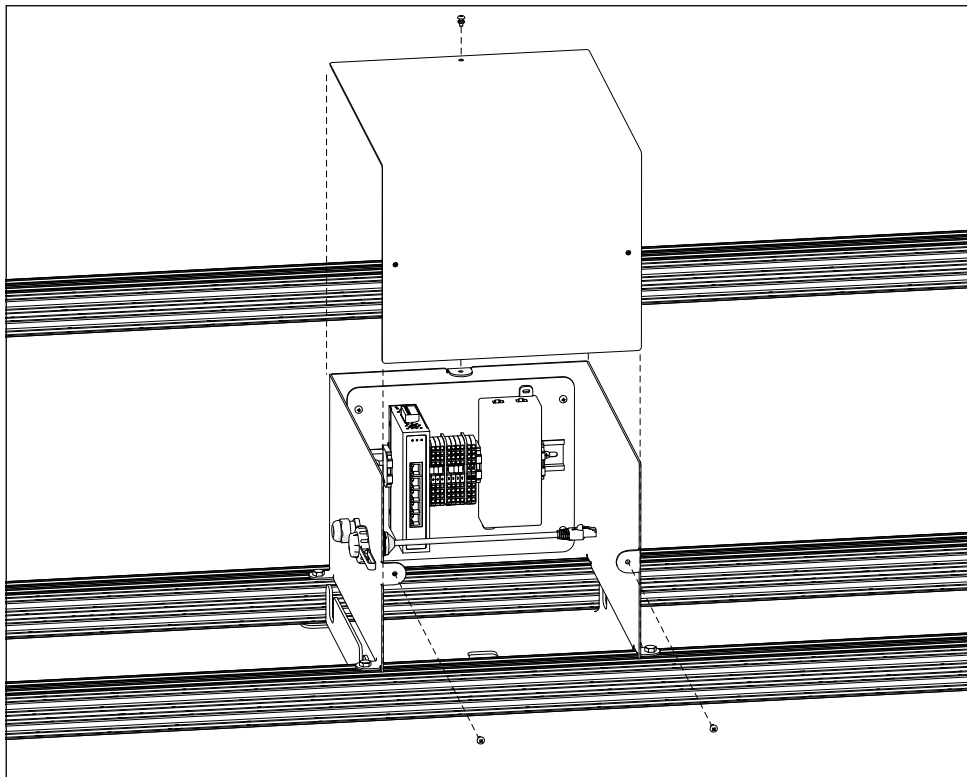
Assemblage du couvercle de la boîte de connexion
